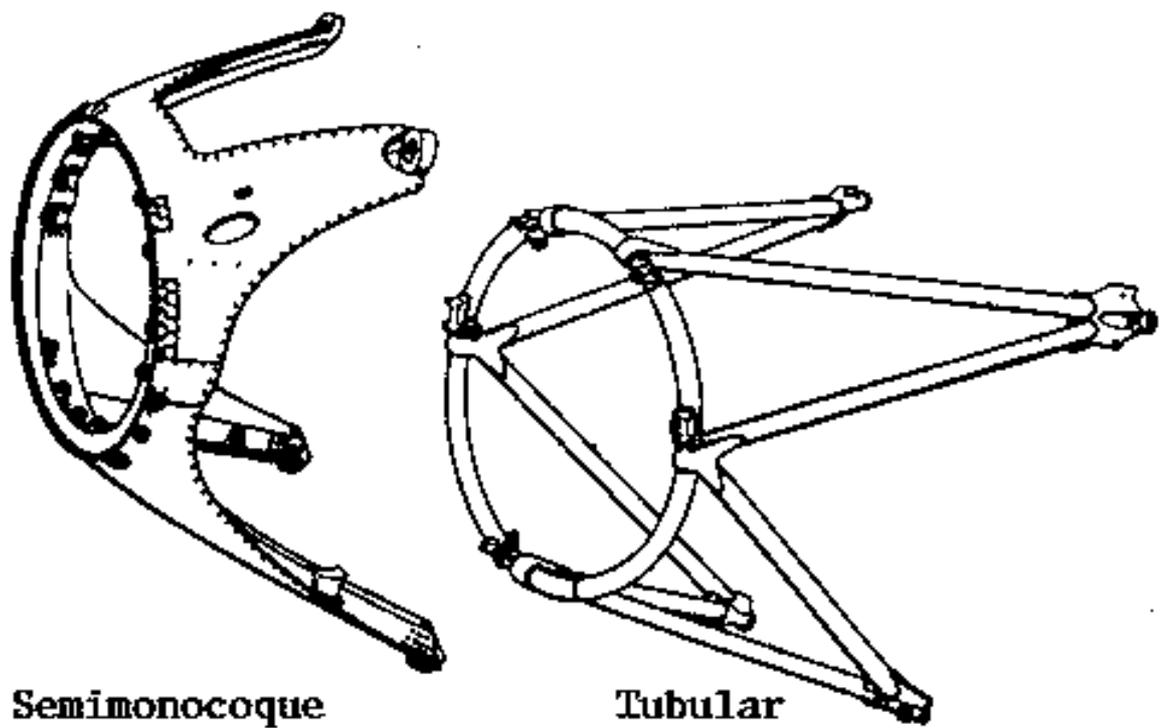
Berços de motor semimonocoque e de tubos de aço soldados.
